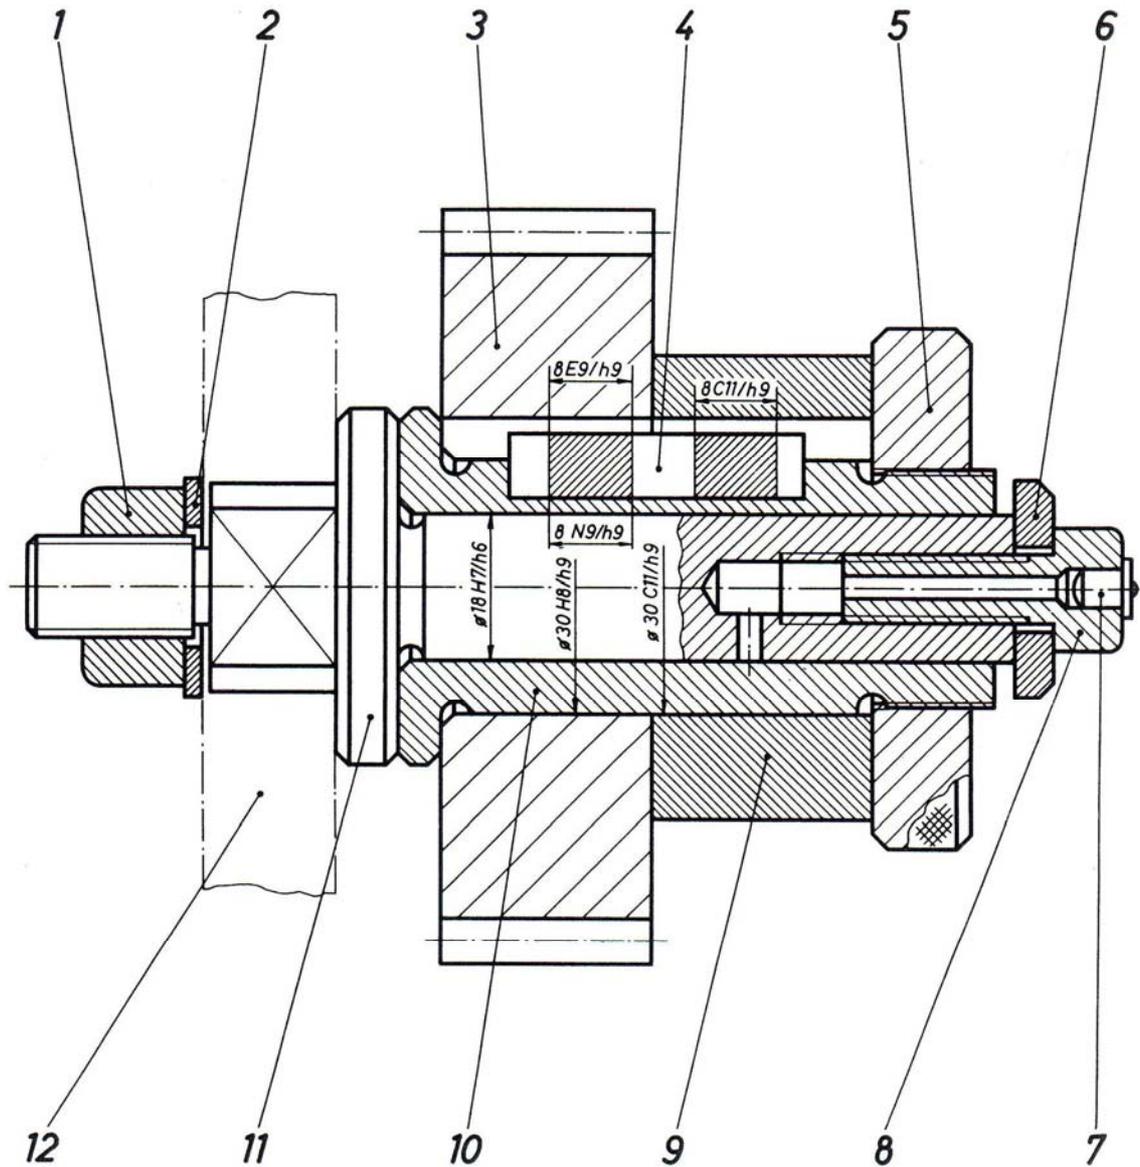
Dibujo de conjunto de mecanismo clásico de acoplamiento de engranajes
